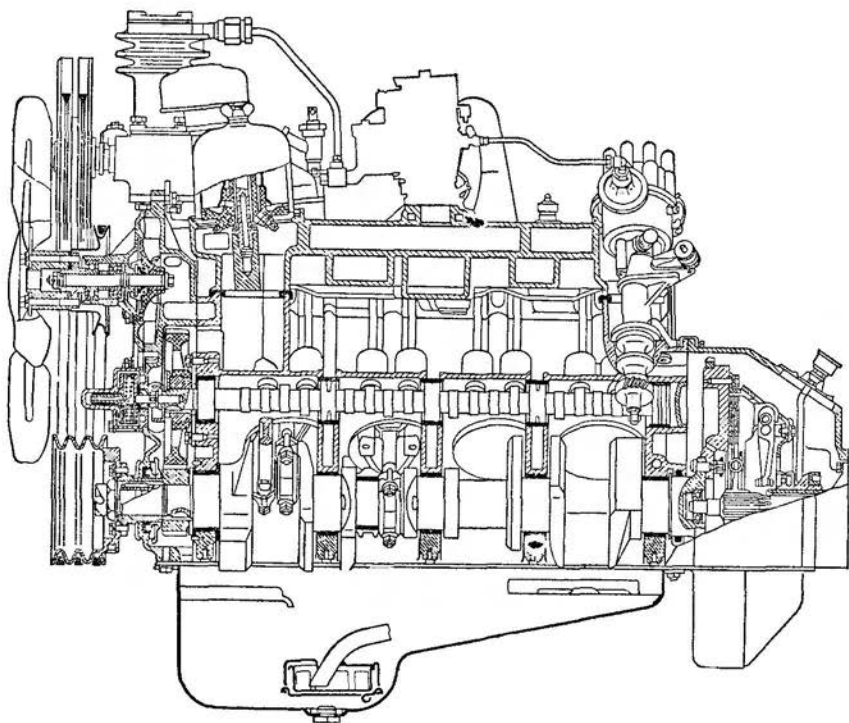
Продольный разрез двигателя автомобиля ГАЗ-66
